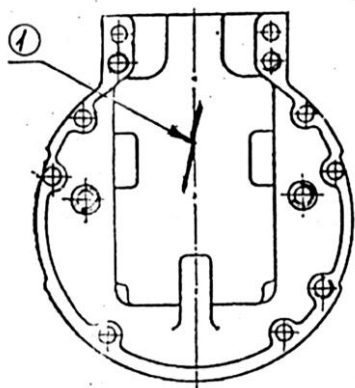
Крышка торцевая регулятора оборотов
